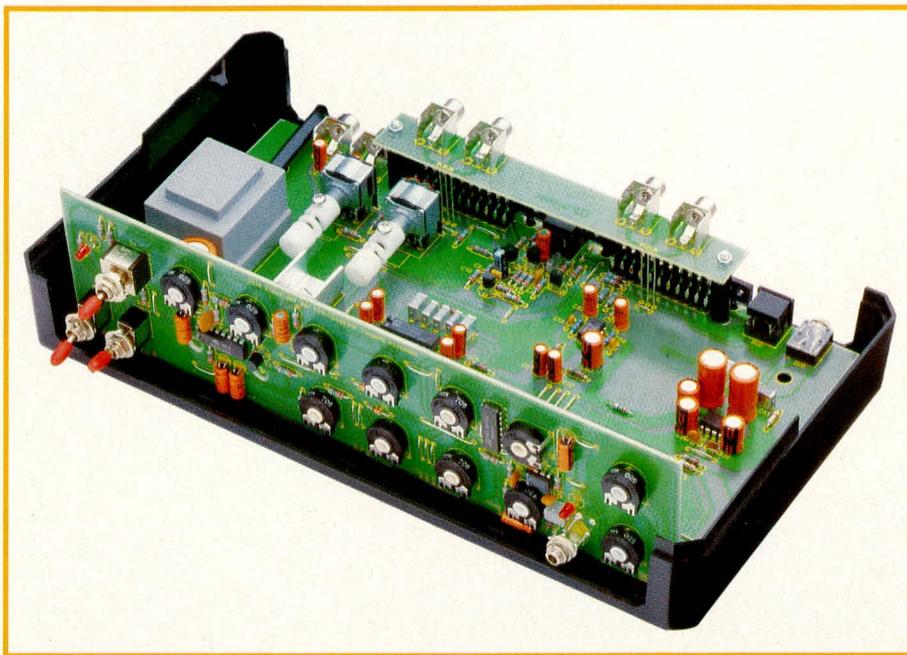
Innensicht des VDM 7000 vor Aufsetzen der oberen Halbschale. Die Montage erfolgt mit einem Minimum an Einzelteilen.
